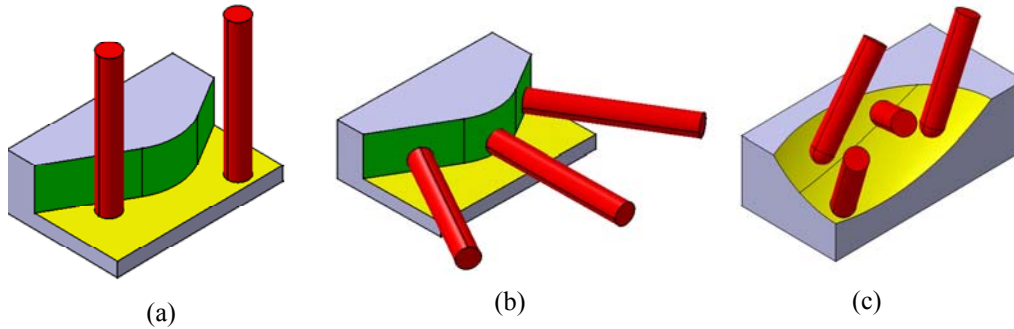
a - Usinage en bout (UEB) ; b - Usinage en flanc (UEF) ; c - Un exemple d'usinage quelconque (UQ)
